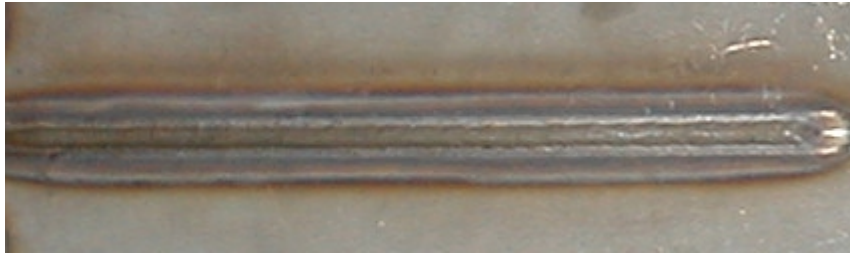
Vista superior del cordón de soldadura de la muestra enfriada en aire agitado
